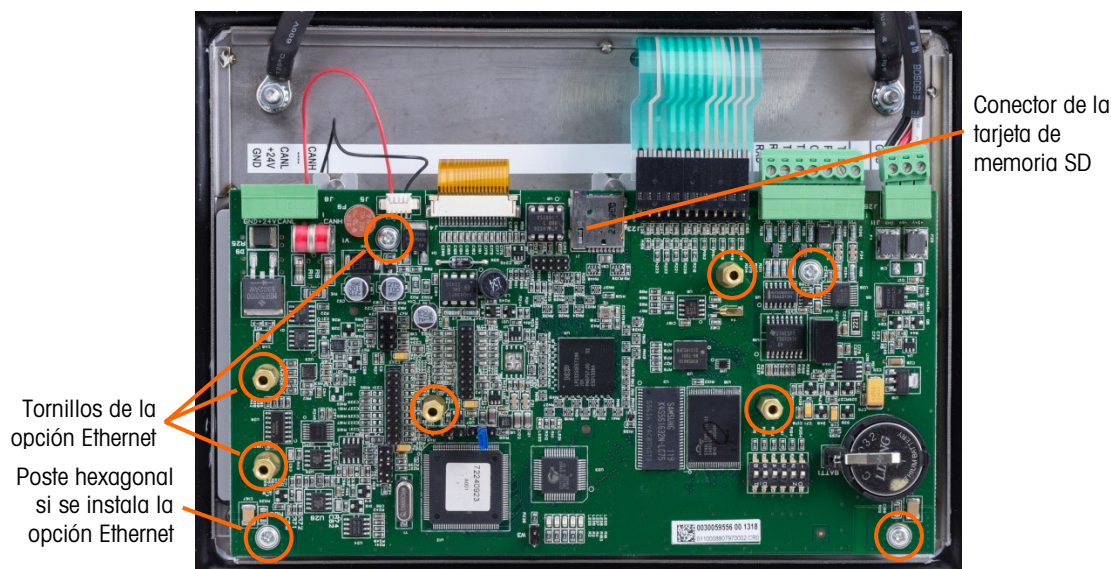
Tornillos de montaje para la tarjeta principal, versión POWERCELL
